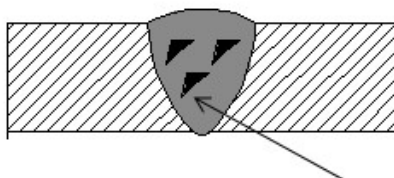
Дефекти зварювання шлакових включень
